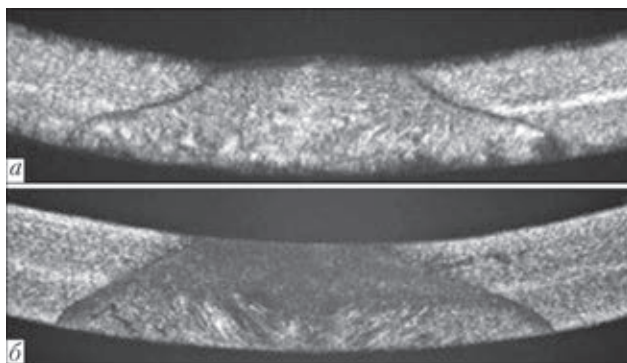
Макроструктура ( $\times 12$ ) сварных соединений труб 20×0,8 мм из стали TP 316L: а — недеформированный шов; б — деформированный
